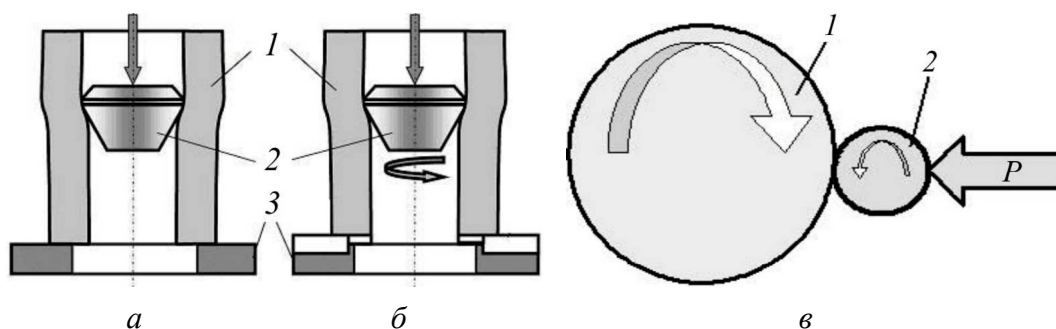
Схема деформирующего протягивания (а), протягивания с вращением (б) и накатки (в): 1 – образец, 2 – инструмент, 3 – опора
